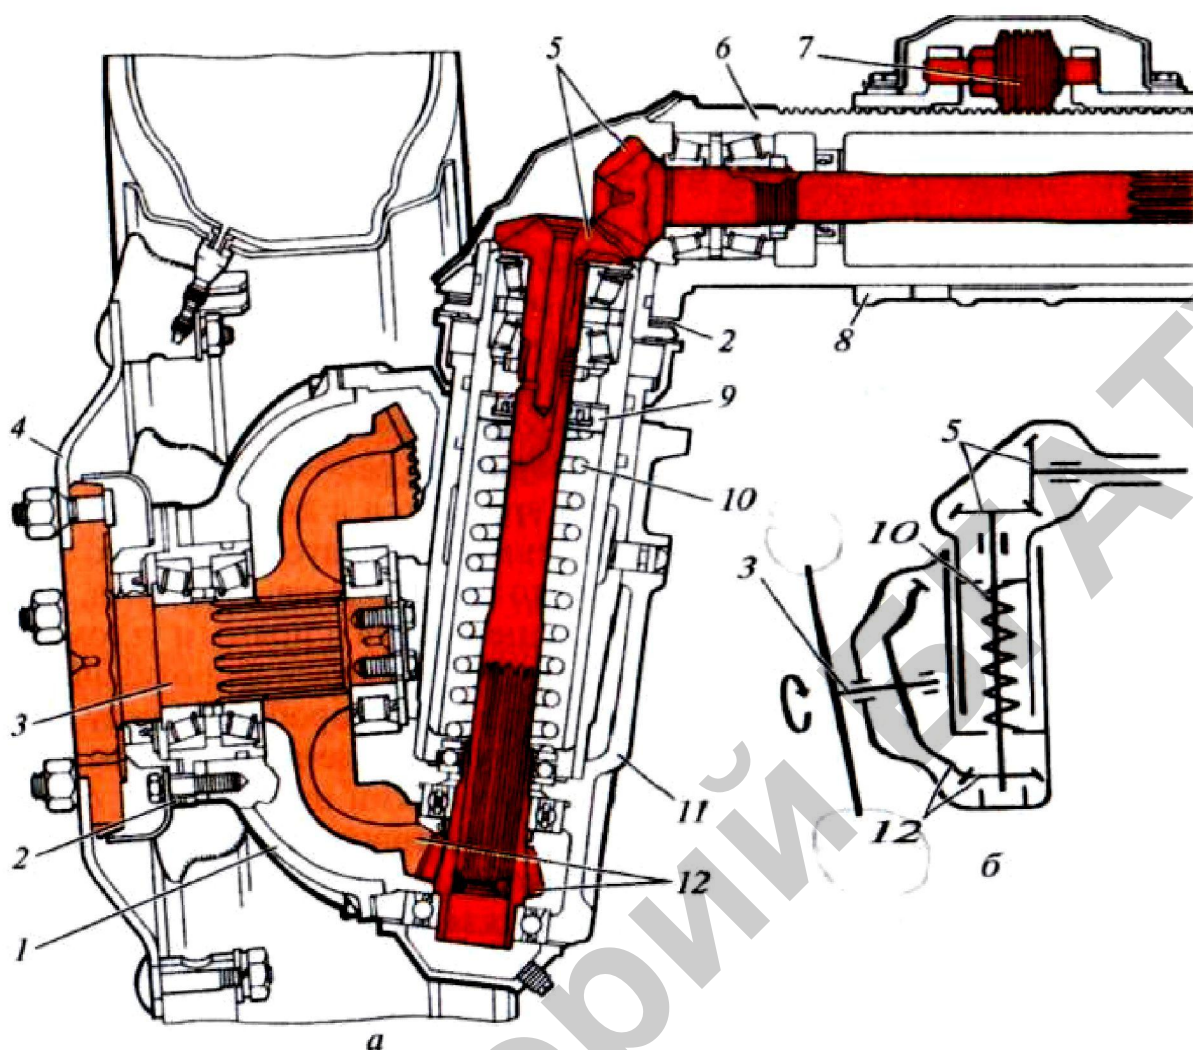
Колесный редуктор переднего ведущего моста трактора «БЕЛАРУС-82.1»:
